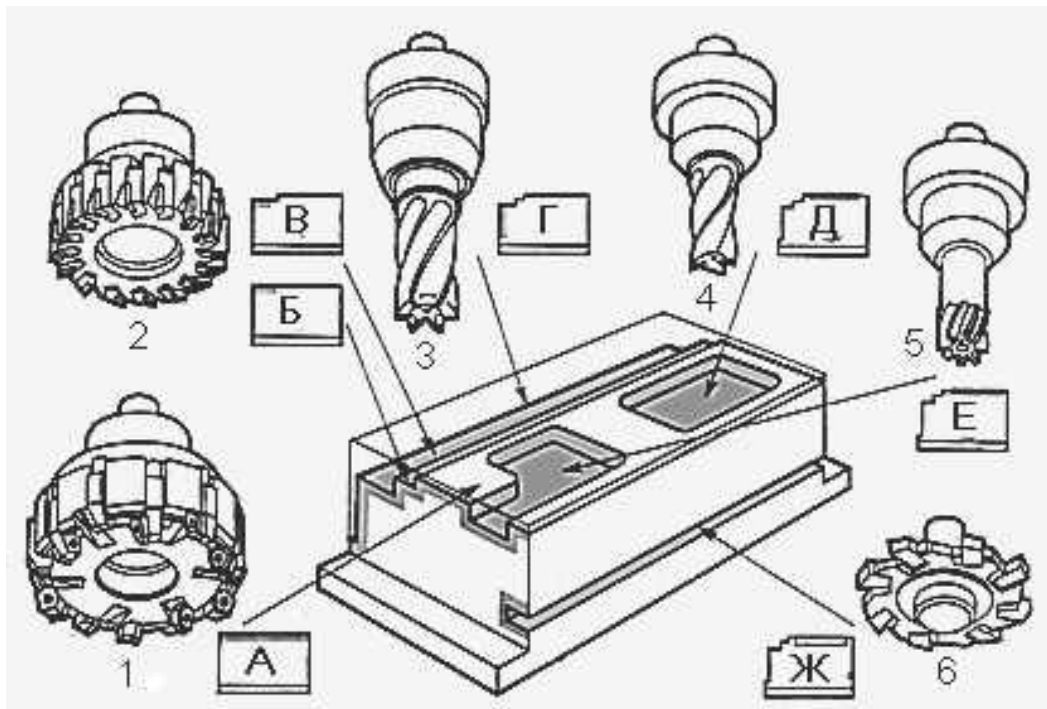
Інструмент для оброблення деталі типу «Корпус»: 1 – фреза торцева; 2 – фреза торцева зі вставними ножами з прямим кутом; 3 – фреза кінцева швидкорізальна; 4 – фреза кінцева швидкорізальна із торцевими зубами; 5 – фреза кінцева швидкорізальна; 6 – фреза кінцева пазова із твердосплавними вставними ножами
